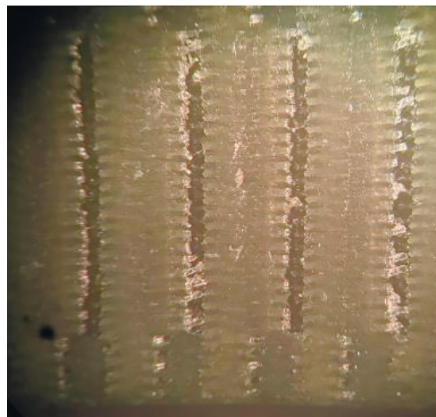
Наихудшая шероховатость при фрезеровании периферией фрезы
